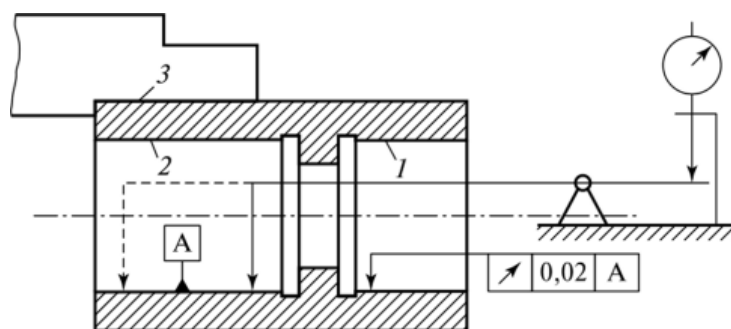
Схема выверки положения втулки на внутришлифовальном станке
